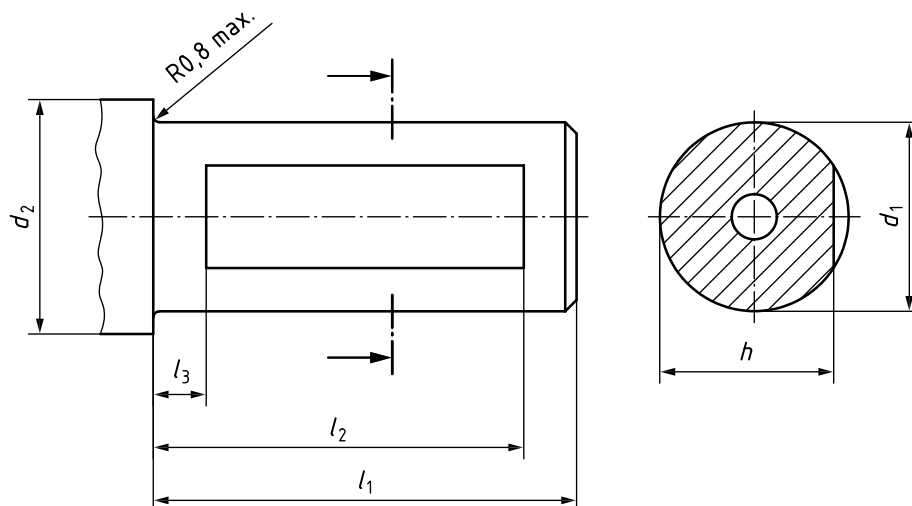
Exemple de queue cylindrique à méplat pour forets à plaquettes amovibles
